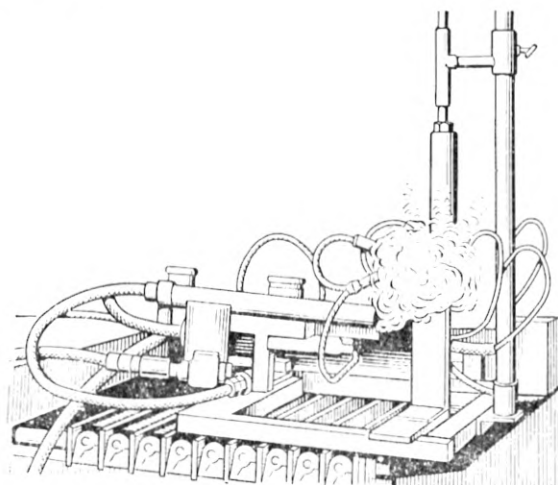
Приспособление для механизированной пайки изделий с трубчатыми соединениями
